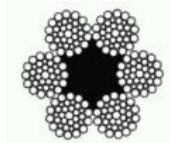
Сечение стального каната двойной свивки типа ЛК-РО
